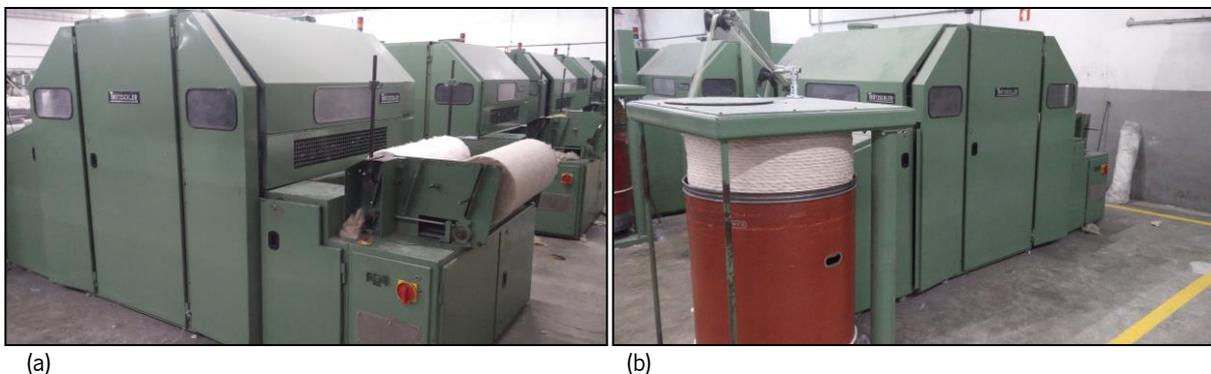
(a) Carda - vista retaguarda; (b) Carda - vista frontal.
